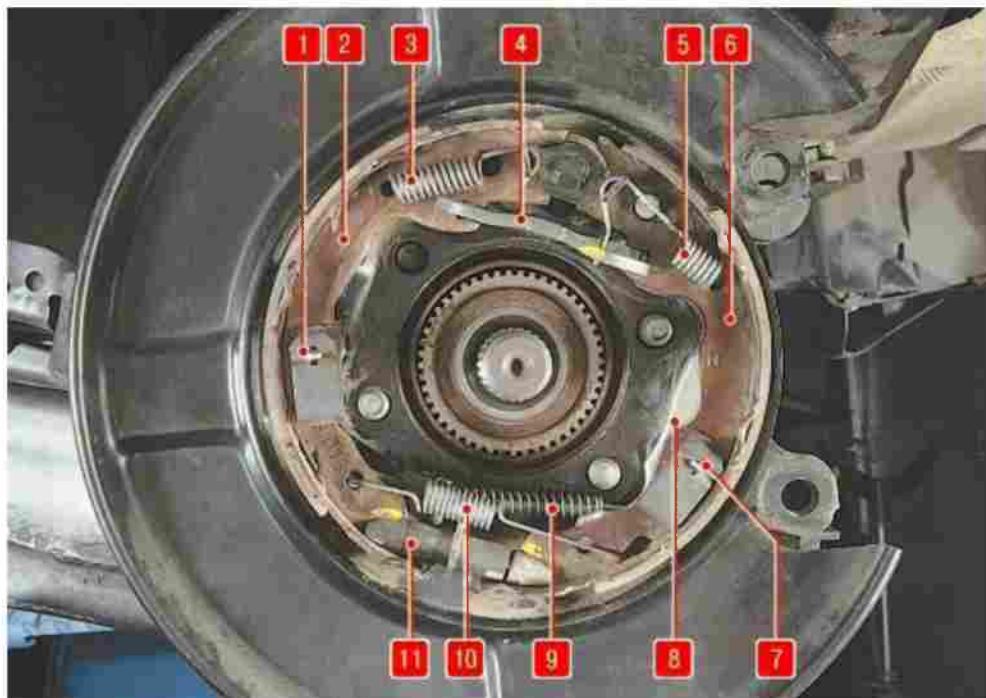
Детали стояночного тормозного механизма: 1, 7 – опорные стойки колодок; 2 – передняя колодка стояночного тормоза; 3 – верхняя стяжная пружина передней колодки; 4 – разжимная планка; 5 – верхняя стяжная пружина задней колодки; 6 – задняя колодка стояночного тормоза; 8 – разжимной рычаг привода колодок; 9 – задний трос стояночного тормоза; 10 – нижняя стяжная пружина колодок; 11 – регулировочное устройство тормозных колодок стояночного тормоза.
